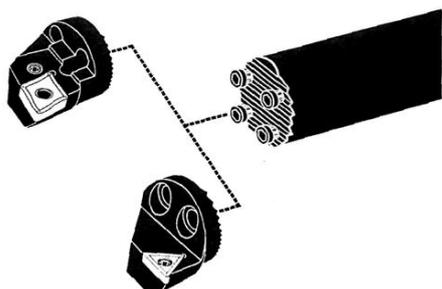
Схема установки и закрепления резцовых модулей посредством болтов и рифлений фирмы «Sandvik Coromant»
